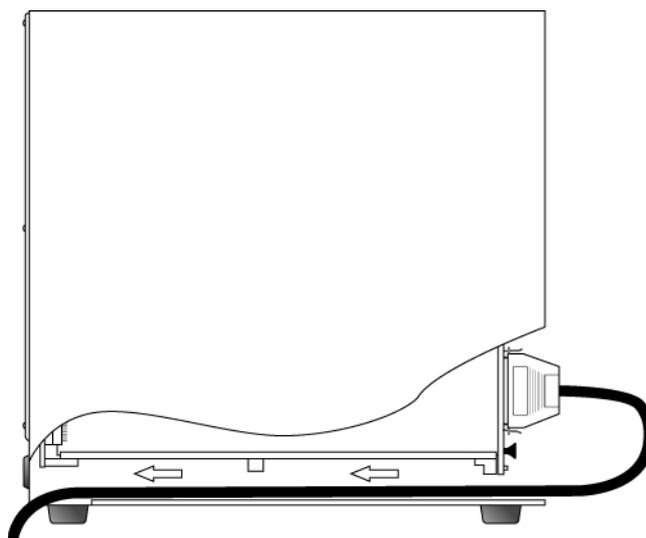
Прокладка соединительных кабелей в корпусе
